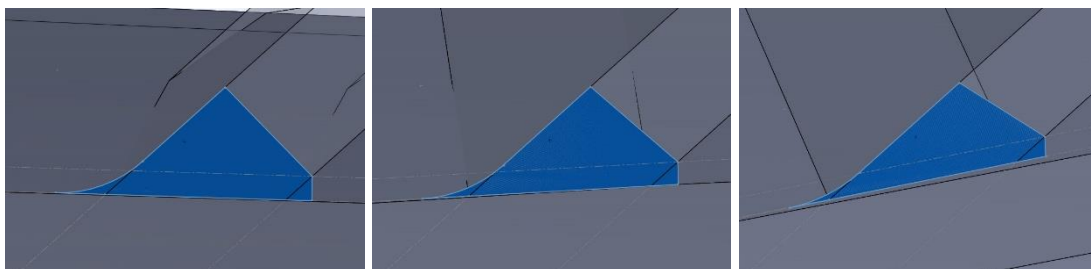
Área de soldadura dibujada sobre el corte creado por el plano de soldadura (Fuente: Propia)
